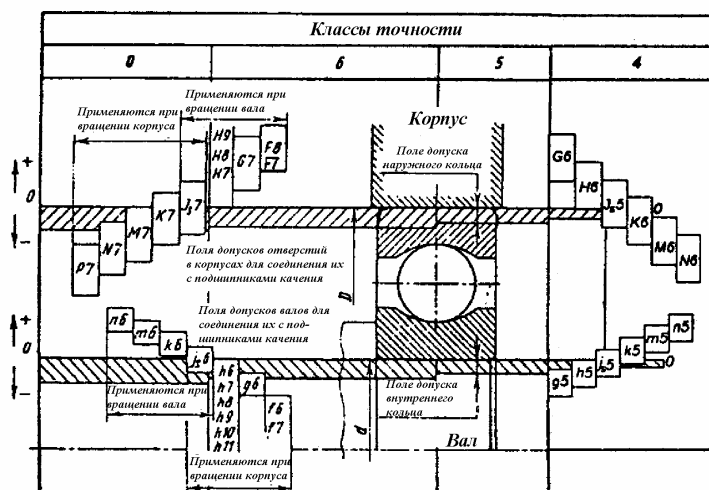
Схема расположения полей допусков на присоединительные размеры подшипников, вала и корпуса
